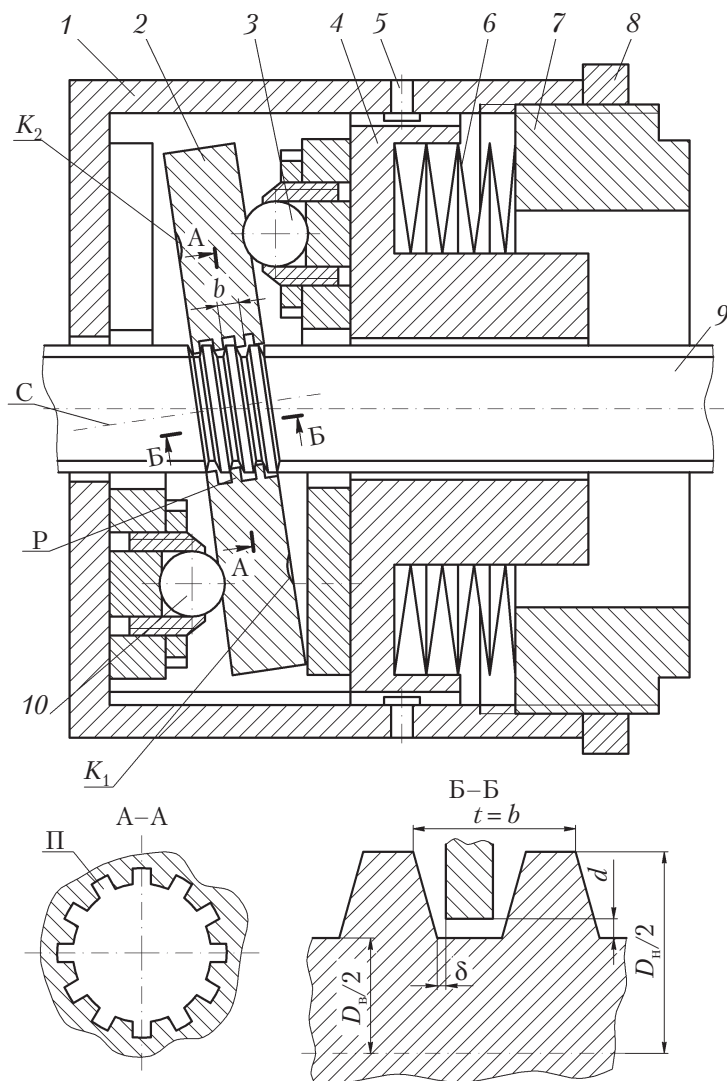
Устройство для виброударного обкатывания винтовых поверхностей
